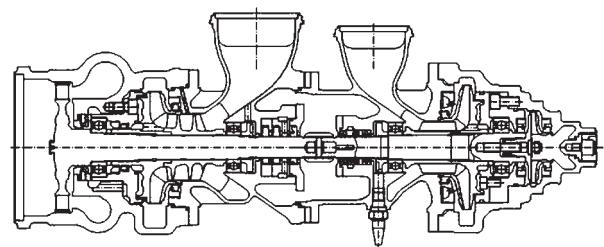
Конструктивная схема двигателя ТНА РД0124
